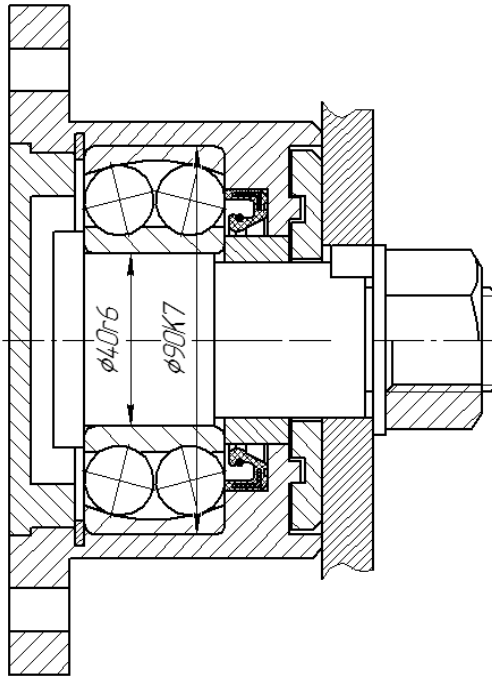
Підшипник типу 1608 – у зборі з підшипниковим вузлом
